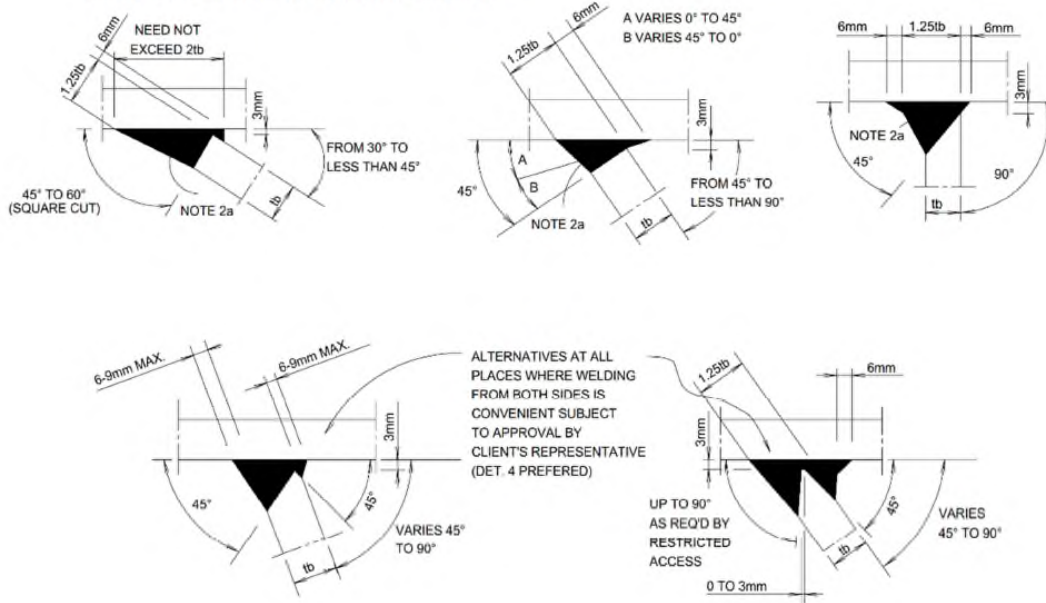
Darstellung der Schweißnahtvorbereitung und Schweißnahtgeometrievorgaben; Auszug aus DNVGL-RPC203 [9] für beidseitig geschweißte Anschlüsse
